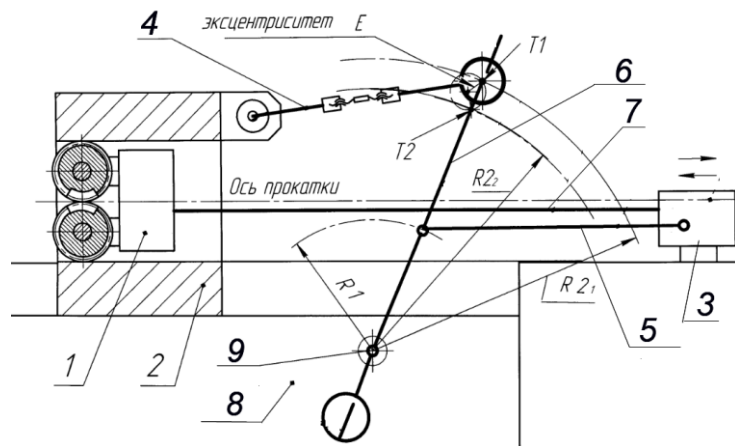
Рабочая линия холодно-пильгерного стана [9]: 1 – сепаратор с вальками (роликами); 2 корпус; 3 – прямолинейный узел привода; 4-7 – рычажная (кулисная) система привода взаимного перемещения корпуса и сепаратора; 8 – станина; 9 – точка крепления кулисного механизма к станине
